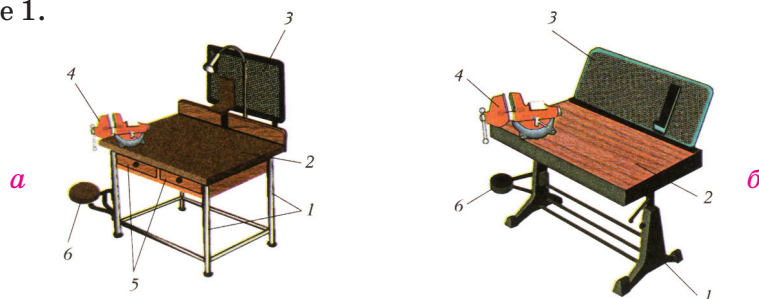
Верстаки: а – слесарный; б – комбинированный:
